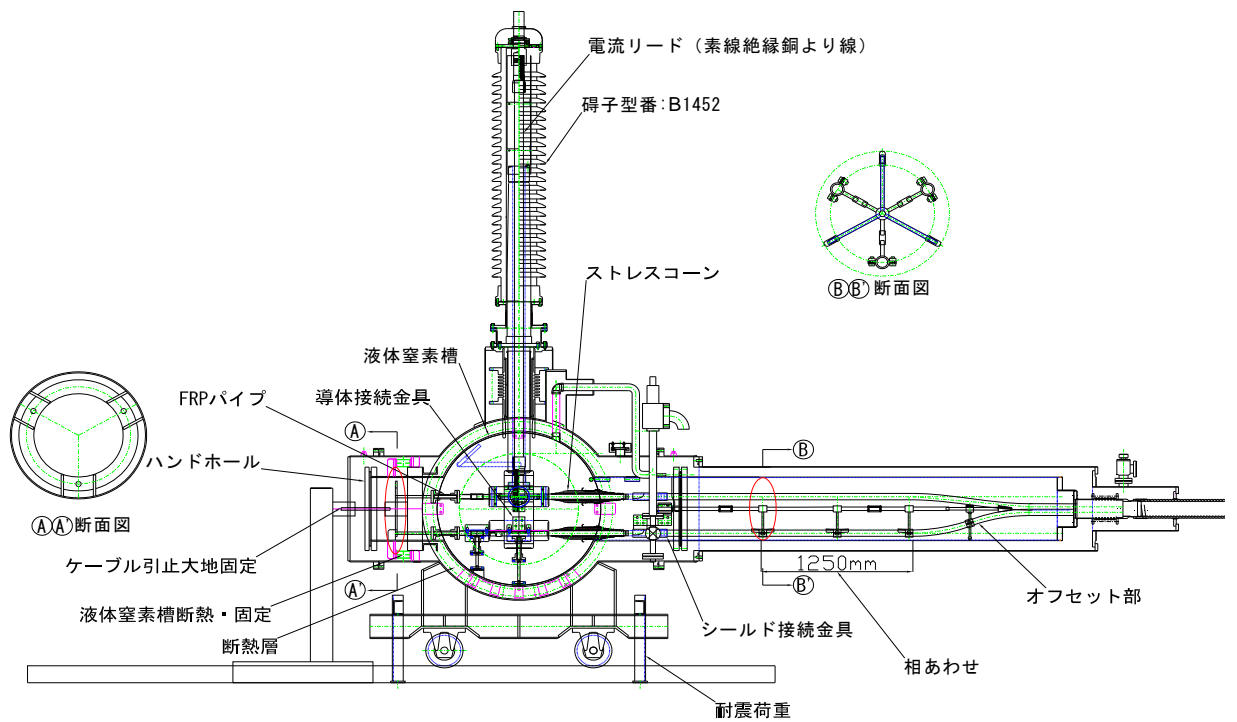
終端接続部の概略構造図 (側面図)
